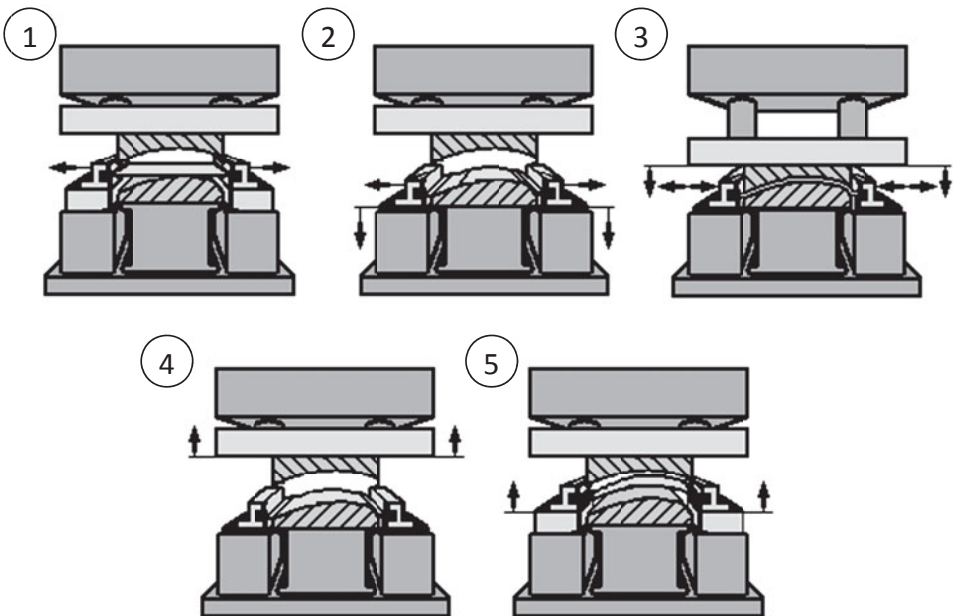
Prinzipielle Darstellung des Tangential-Streckziehens in einer einfach-wirkenden hydraulischen Presse. Quelle: Fa. Cyril Bath, USA
